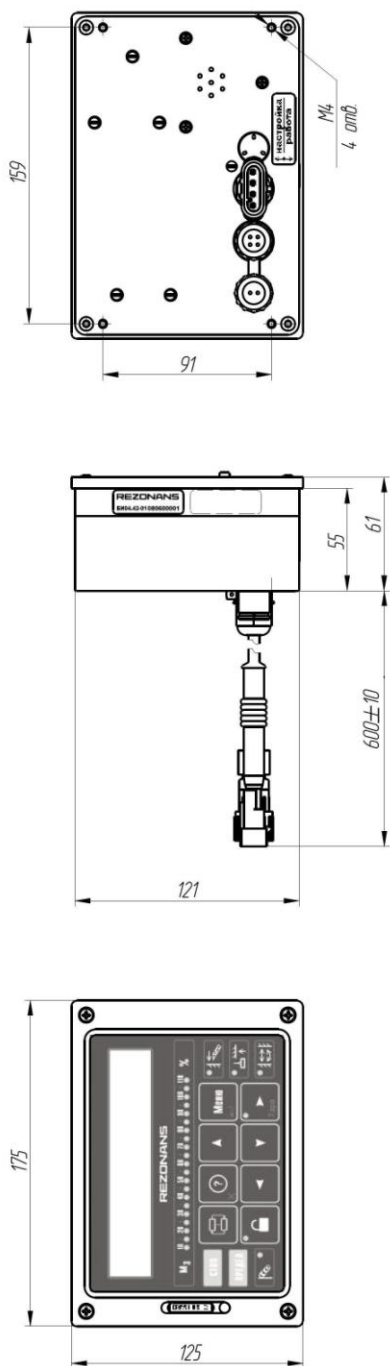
Габаритные и присоединительные размеры блока индикации БИ04.42-01
